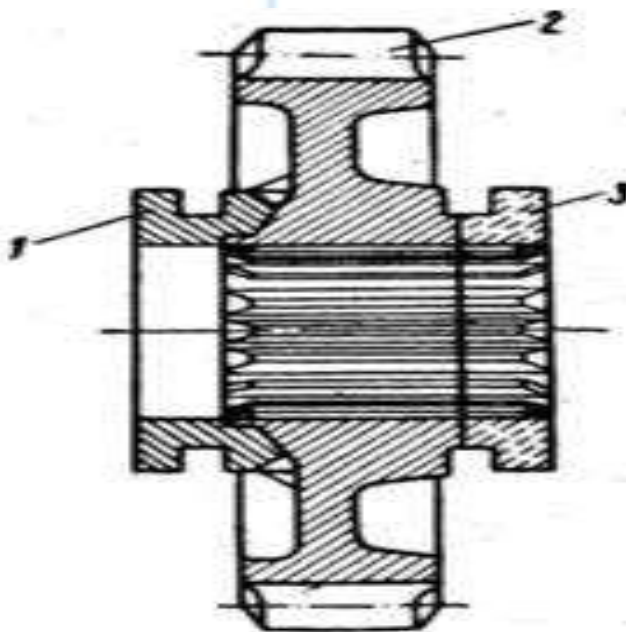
Ремонт зубчатого колеса способом перевёртывания.
